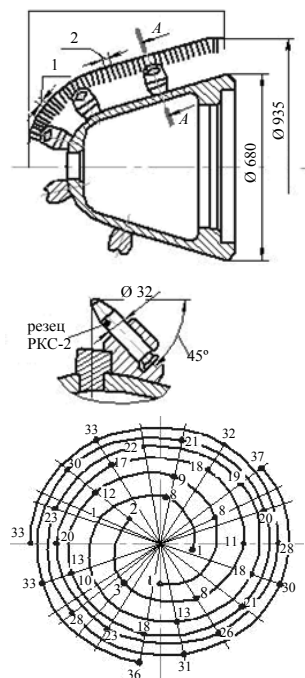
Конструкция продольно-осевой оптимизированной режущей коронки: 1 – 37 – номера резцов
